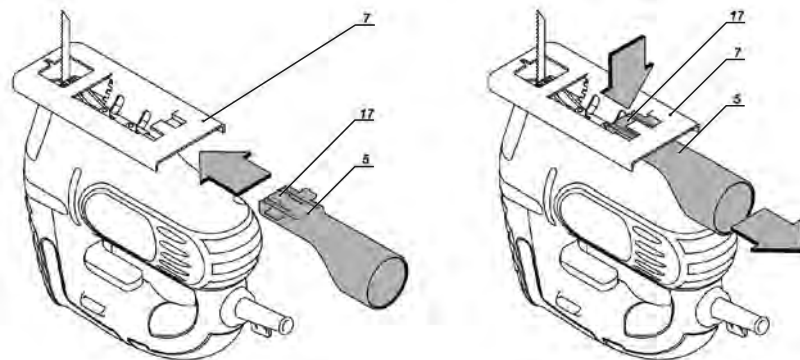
desenho demonstrativo para montagem e desmontagem do adaptador para aspirador de pó
